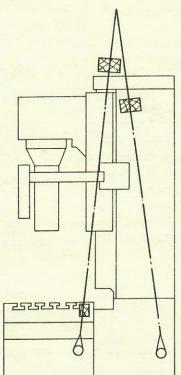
Схема транспортирования станка 2733П Масса станка 3500 кг
